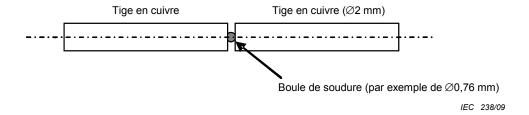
Illustration schématique du joint de soudure seul pour l'essai de fatigue mécanique
